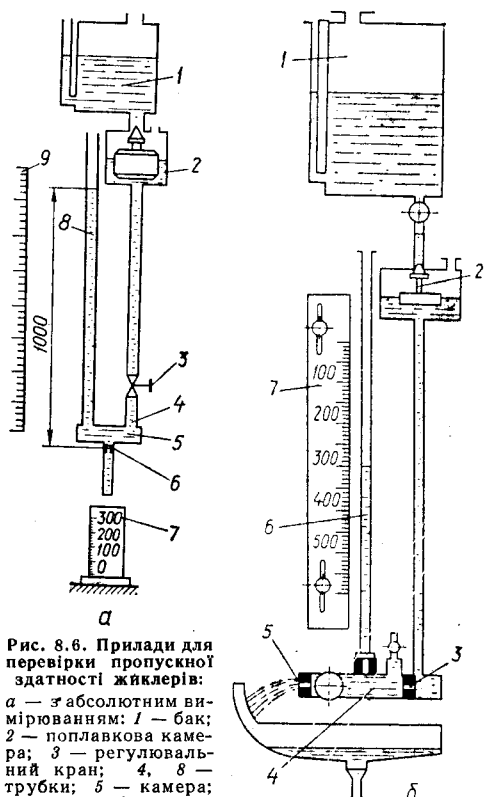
Прилади для перевірки пропускної здатності жиклерів: а — з абсолютним вимірюванням: 1 — бак; 2 — поплашкова камера; 3 — регулювальний кран; 4, 8 — трубки; 5 — камера; 6 — випробувуваний жиклер; 7 — мензурка; 9 — шкала; б — із відносним вимірюванням: 1 — бак; 2 — поплашкова камера; 3 — калібрований отвір; 4 — камера; 5 — випробувуваний жиклер; 6 — контрольна трубка; 7 — шкала
